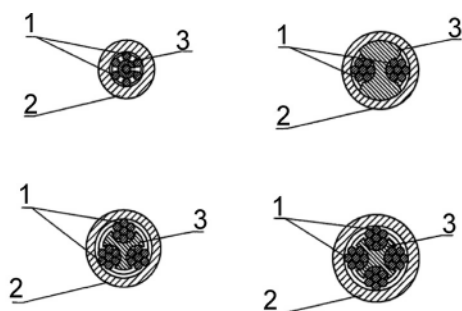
Форми клинів для закріплення каната: 1 – канат; 2 – муфта з'єднувальна; 3 – втулка клинова
